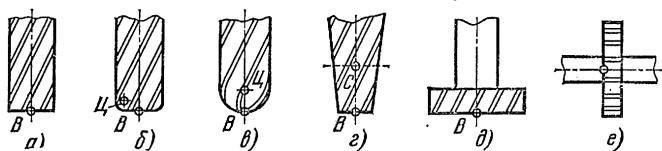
Основные типы фрез для обработки контуров и поверхностей
